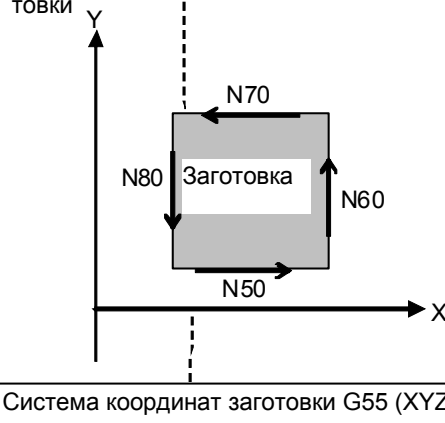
(х) Операция при отсутствии погрешности установки заготовки
